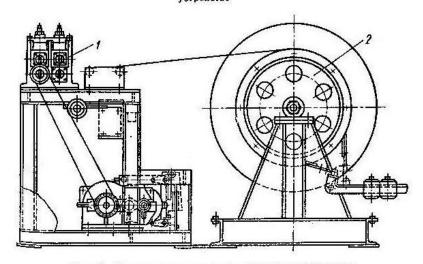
Станок для размотки рулопного металла: 1 — правильно-тянущее устройство, 2 — конусные зажимы-держатели
